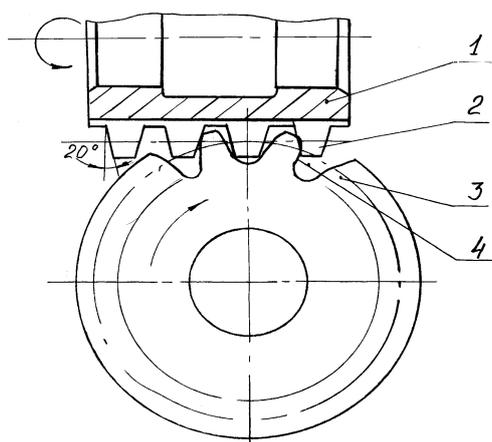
Схема зацепления исходной рейки червячной фрезы с обрабатываемым колесом
